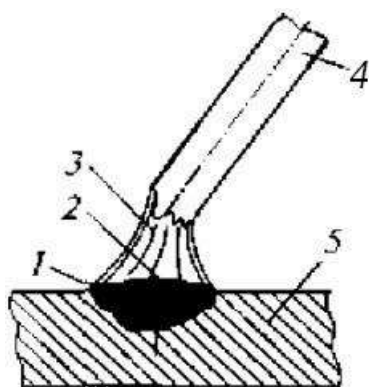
Схема зварювання деталей зварною дугою [18]:
